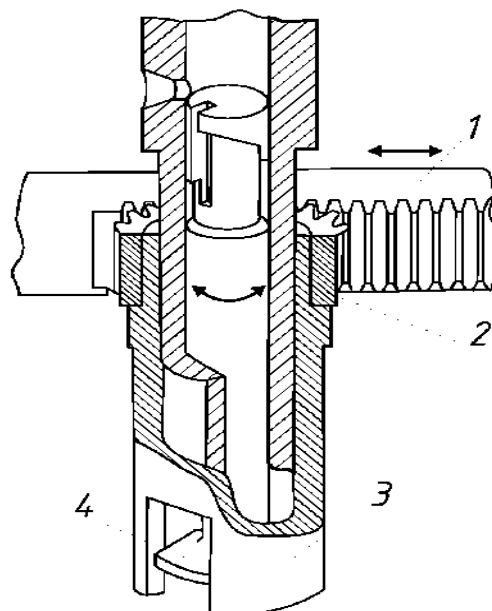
Зубчато-рейкова передача для провертання плунжера:
